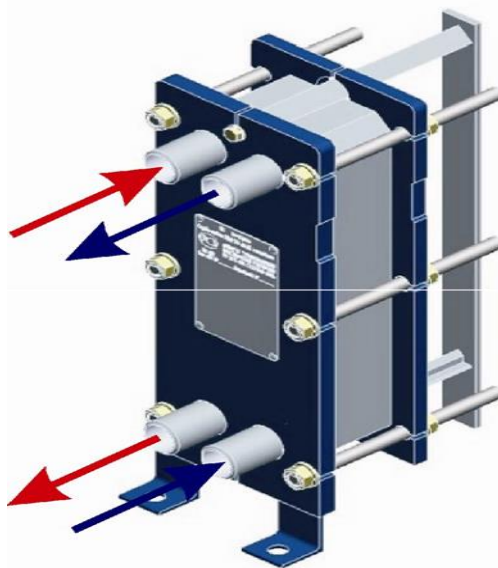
Общий вид пластинчатого подогревателя марки Ридан НН
